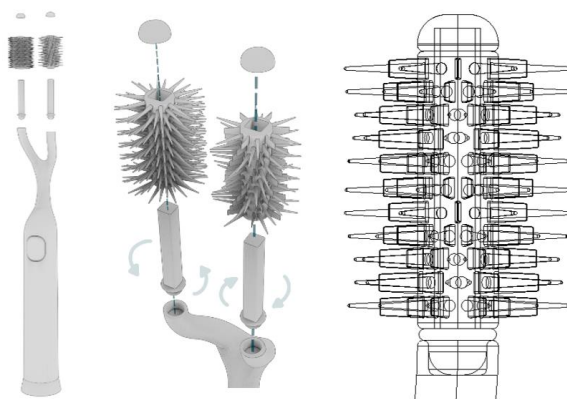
Проработка конструкции сменных насадок с щетинками
